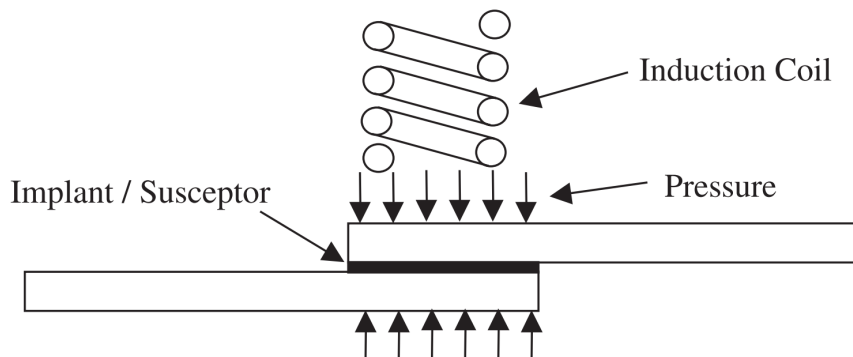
Prinzip des Induktionsschweißens [12, S. 328]
